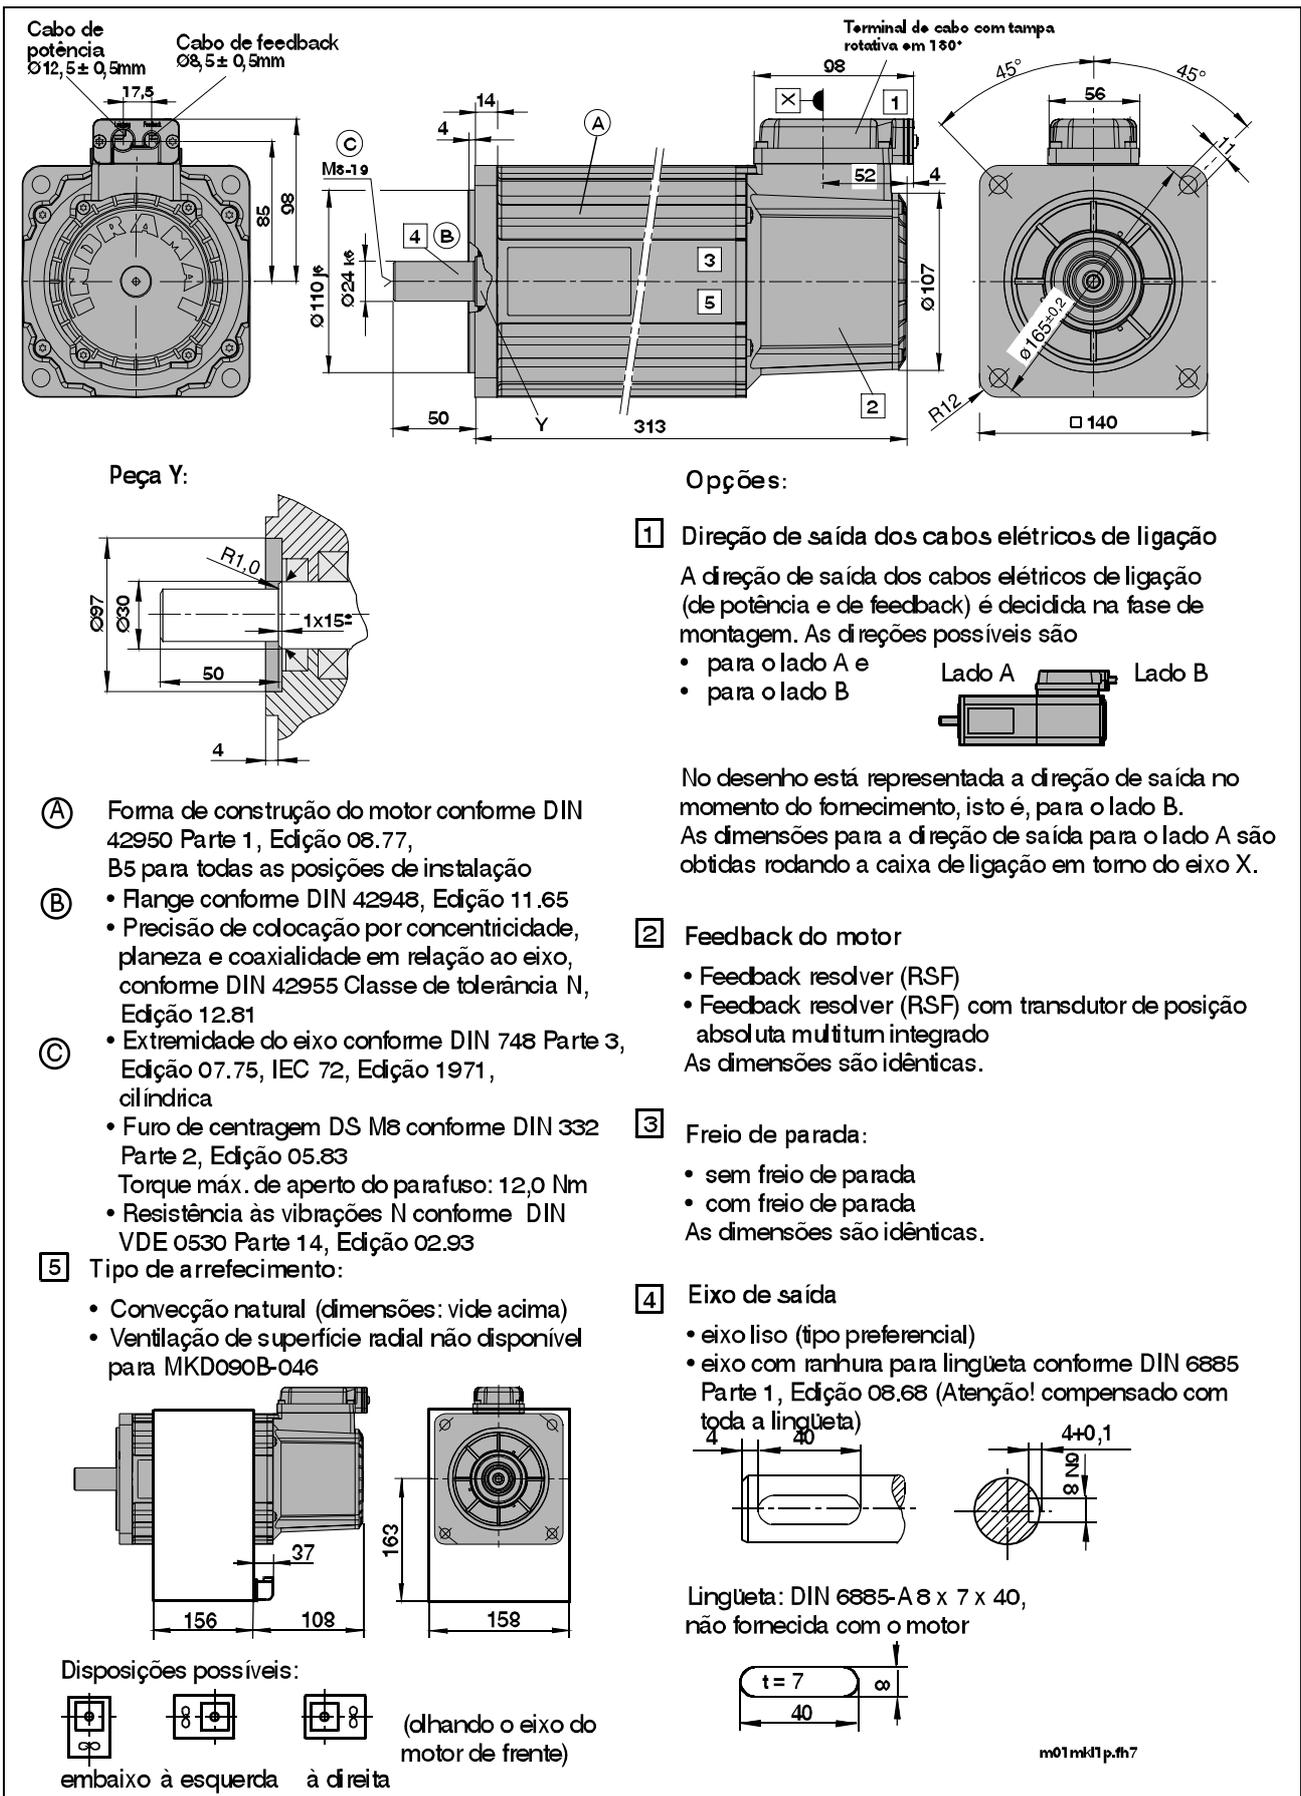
Dimensões MKD090B-035, -046, -047, -058
